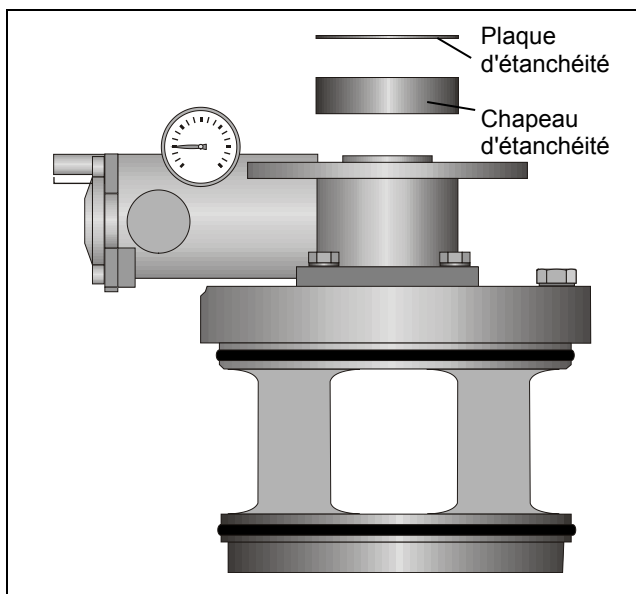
Dépose de la plaque d'étanchéité et du chapeau d'étanchéité
